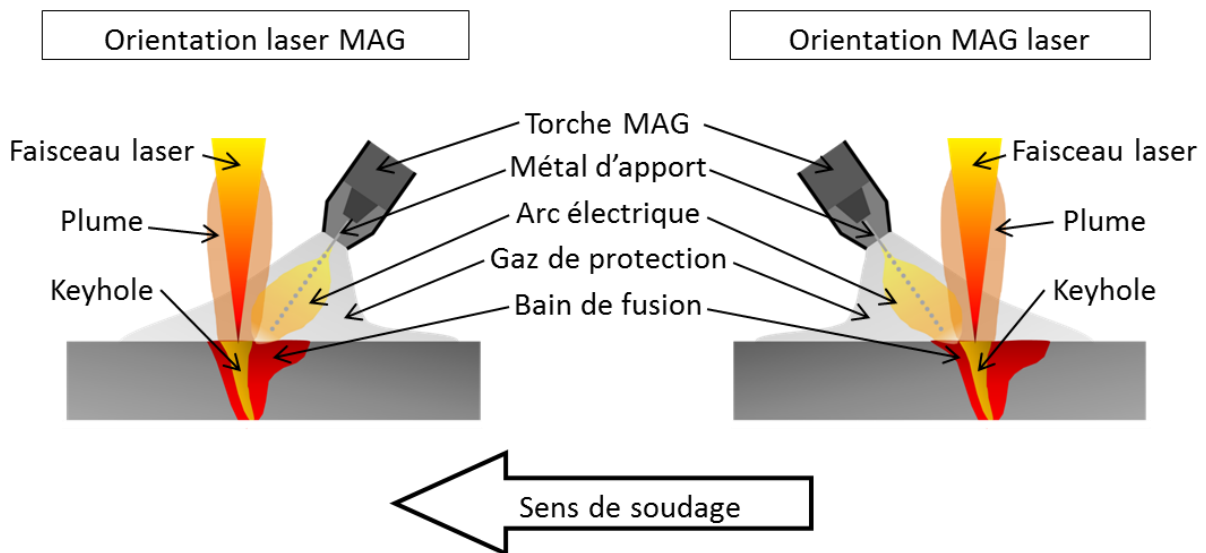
Principe du procédé de soudage hybride laser-MAG
